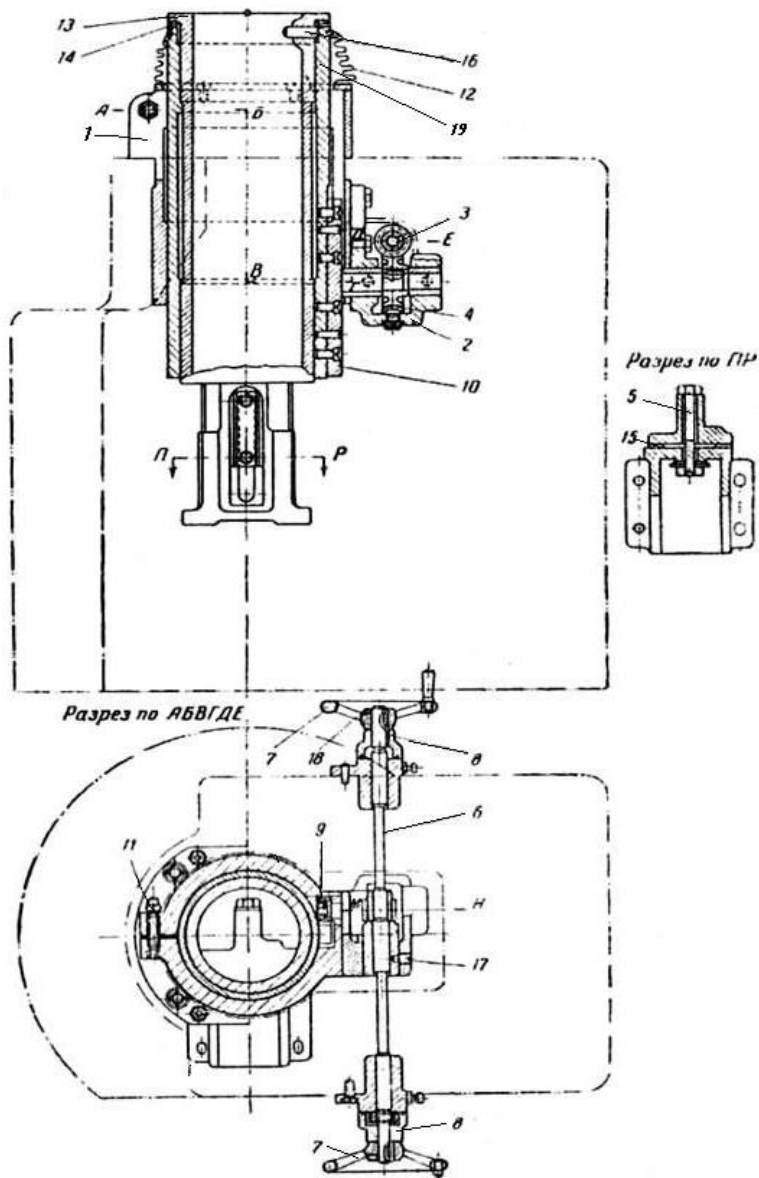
Механизм подъема шлифовальной головки станка мод. 3А642
